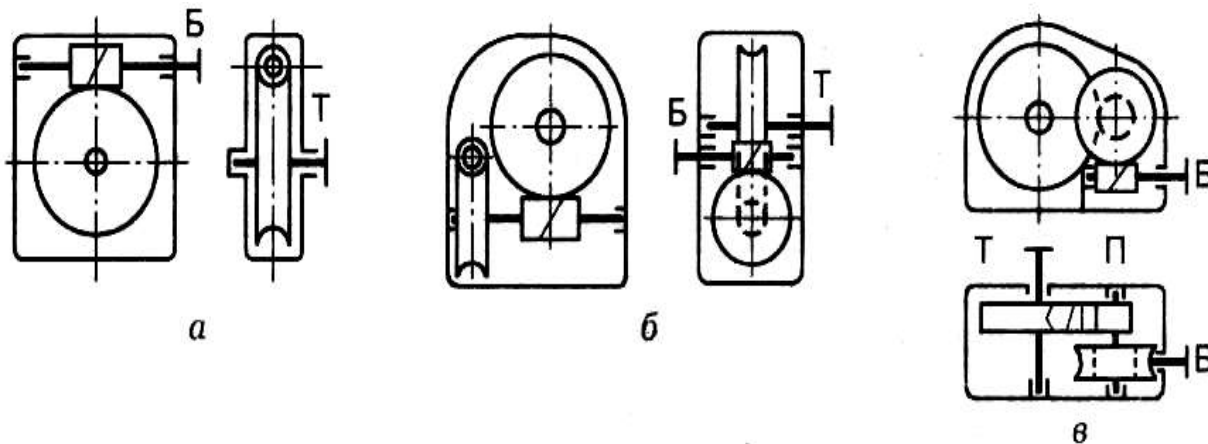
Схемы червячных редукторов: *а* — одноступенчатый; *б* — двухступенчатый; *в* — червячно-цилиндрический
